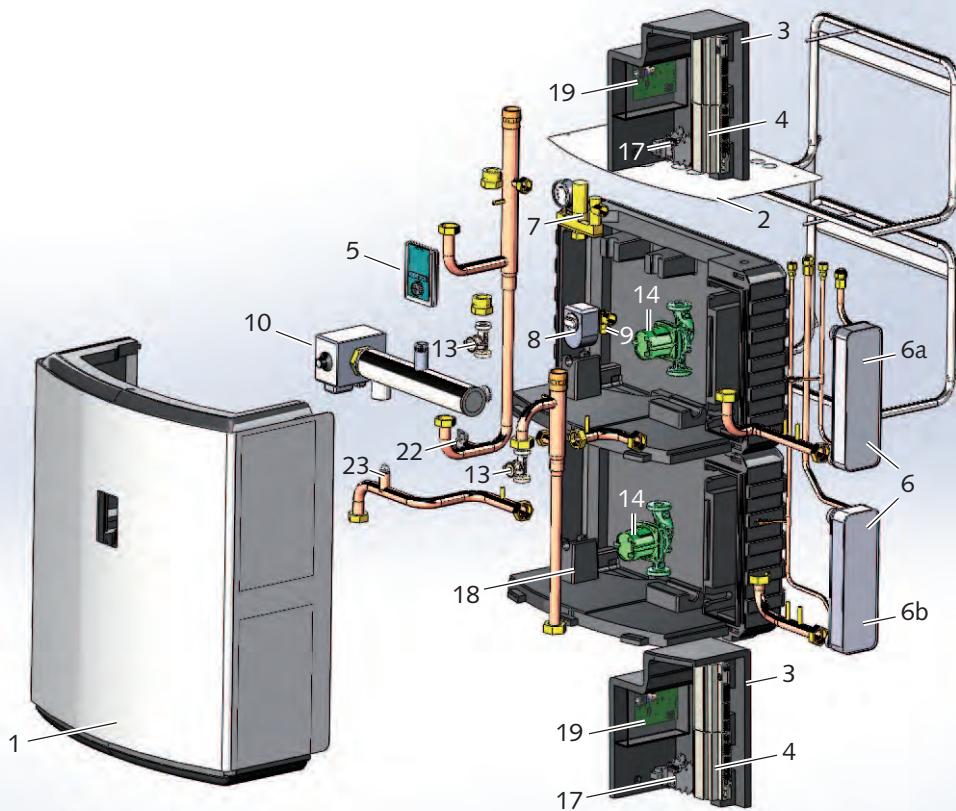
Explosionszeichnung Innenmodul WKF 120/180 Duo
